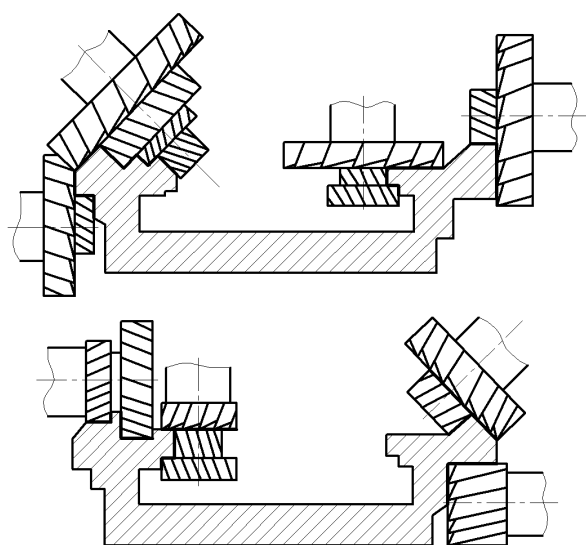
Оброблення напрямних на поздовжньо-фрезерному верстаті
